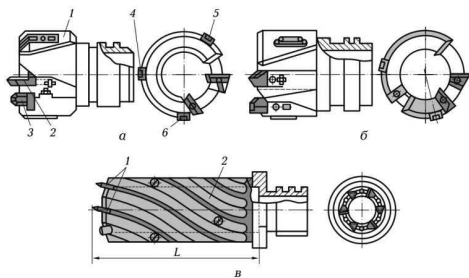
Кільцеві свердла: а – дворізцеві; 1 – корпус; 2, 3 – змінні різці; 4 - 6 – напрямні пластини; б – трірізцеві; в – багаторізцеві; 1 –різці; 2 – корпус; L – довжина робочої частини
